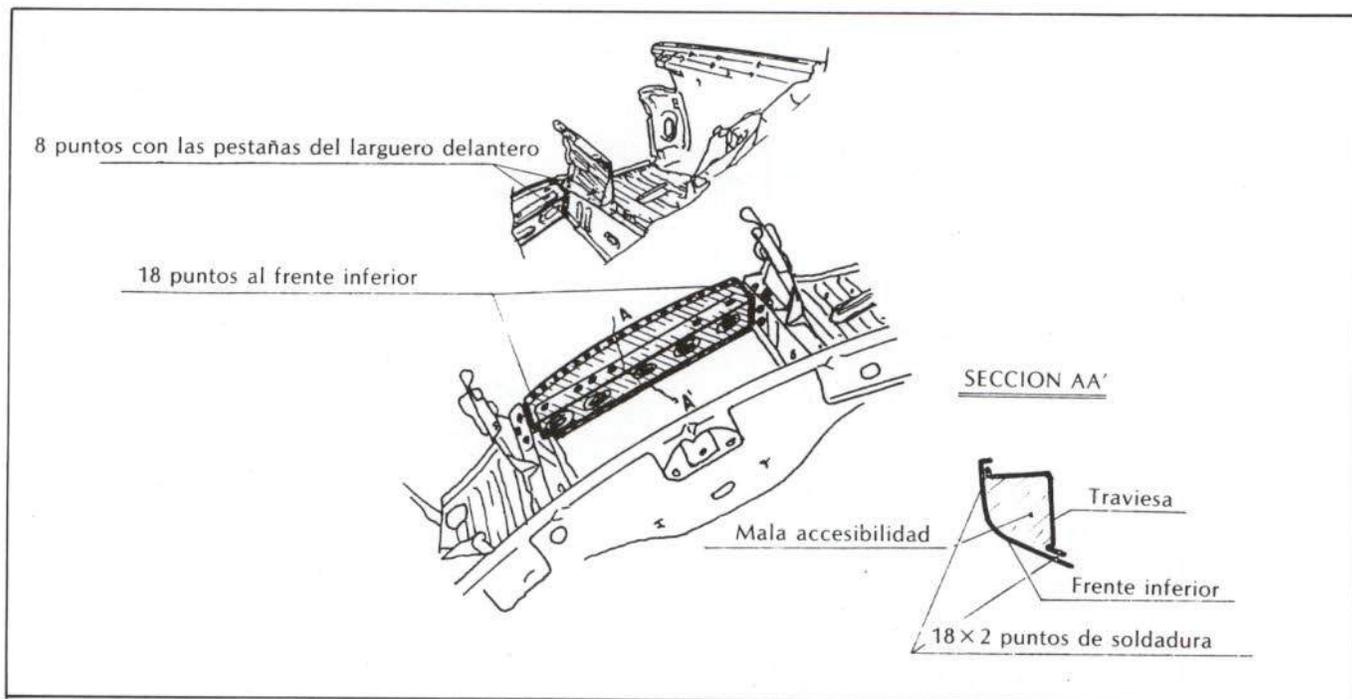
Fijación de la traviesa inferior a carrocería. Accesibilidad.
